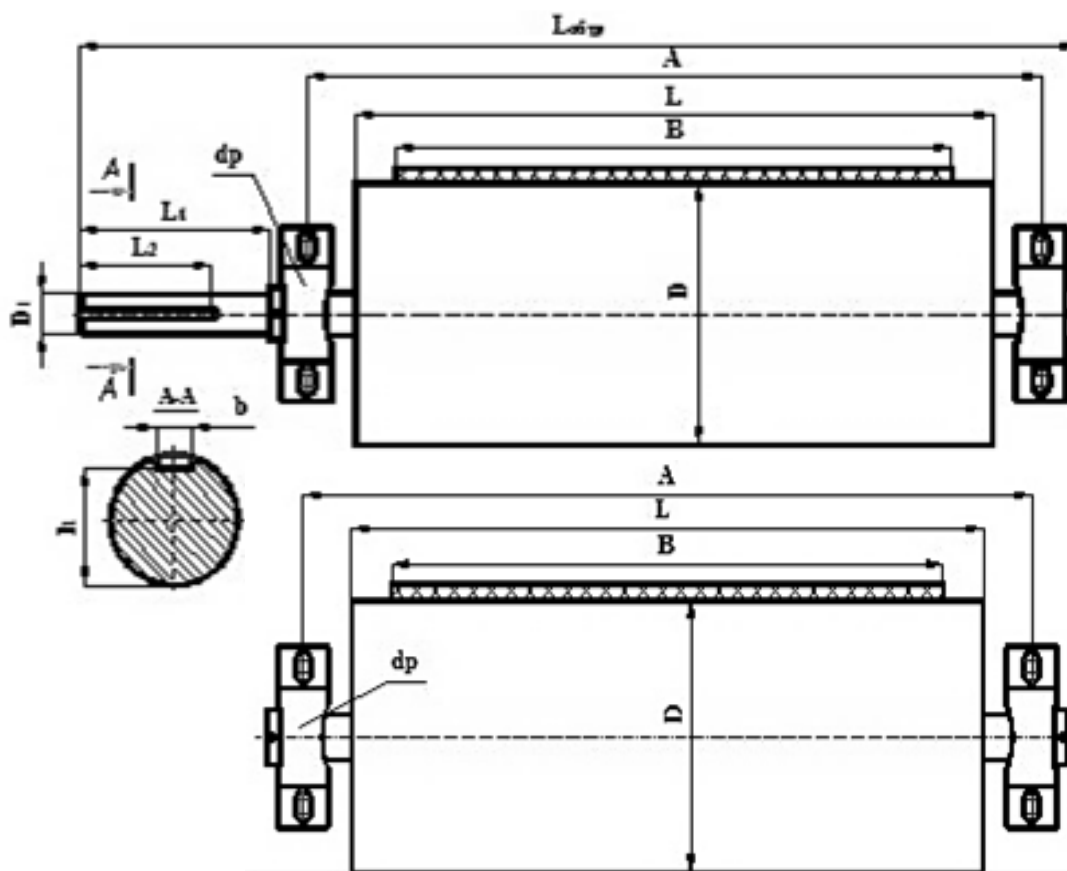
Бочкообразная форма футеровки барабана
